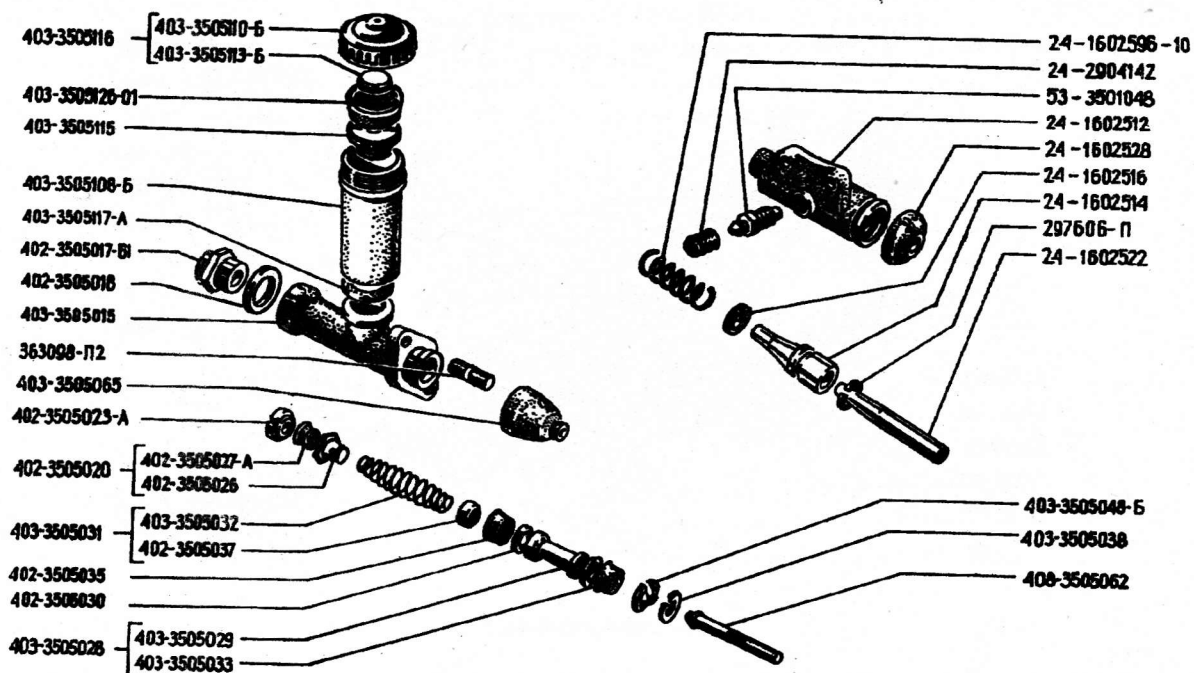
Механизм и привод управления сцеплением, цилиндр главный тормозной
